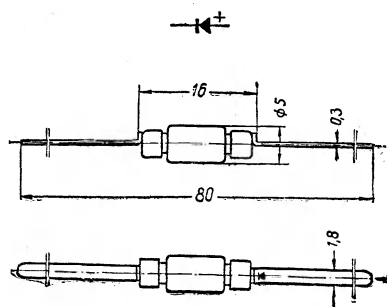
Габаритный чертеж дисков типа Д101—Д103, Д10—Д14
